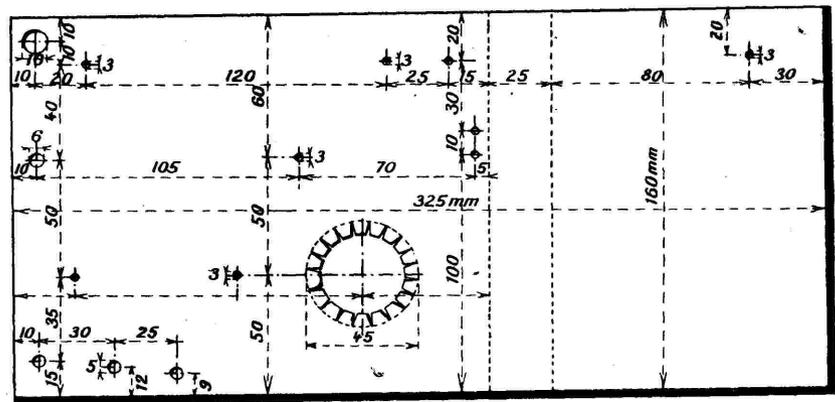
Plan de perçage du blindage intérieur en aluminium de 1 mm.
